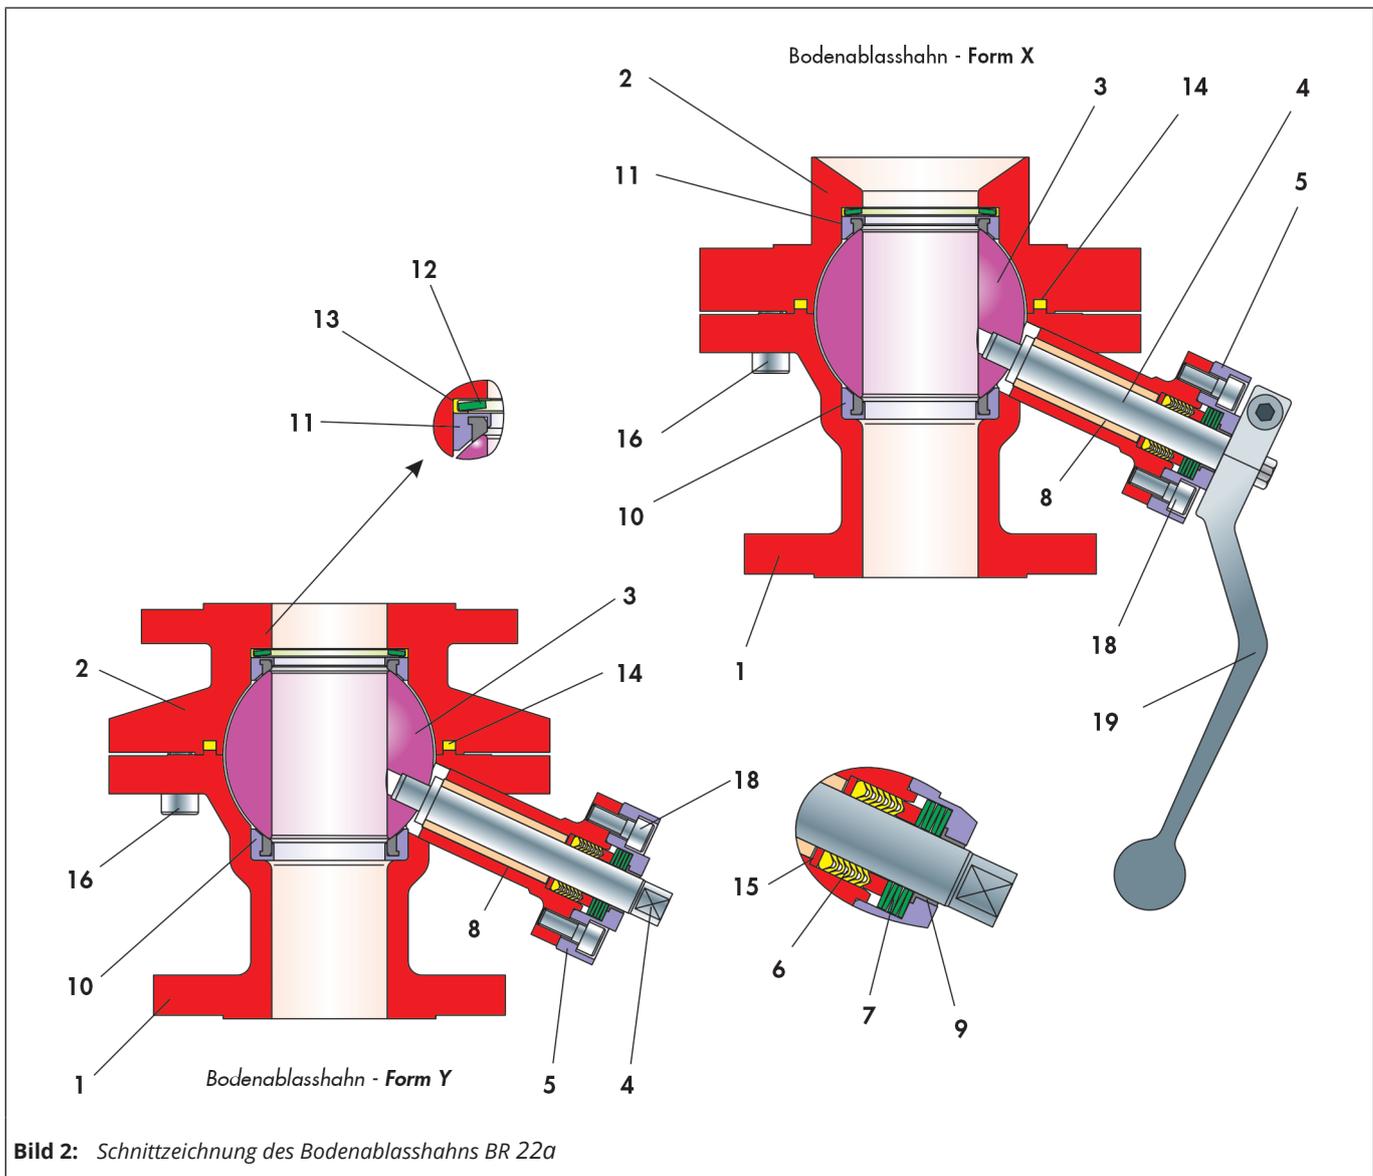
Schnittzeichnung des Bodenablasshahns BR 22a
